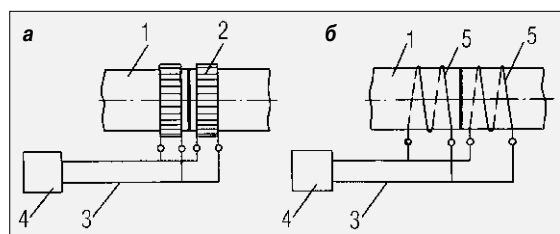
Схемы параллельного соединения электронагревателей ГЭН (а) и КЭН (б) при термообработке сварных соединений:
